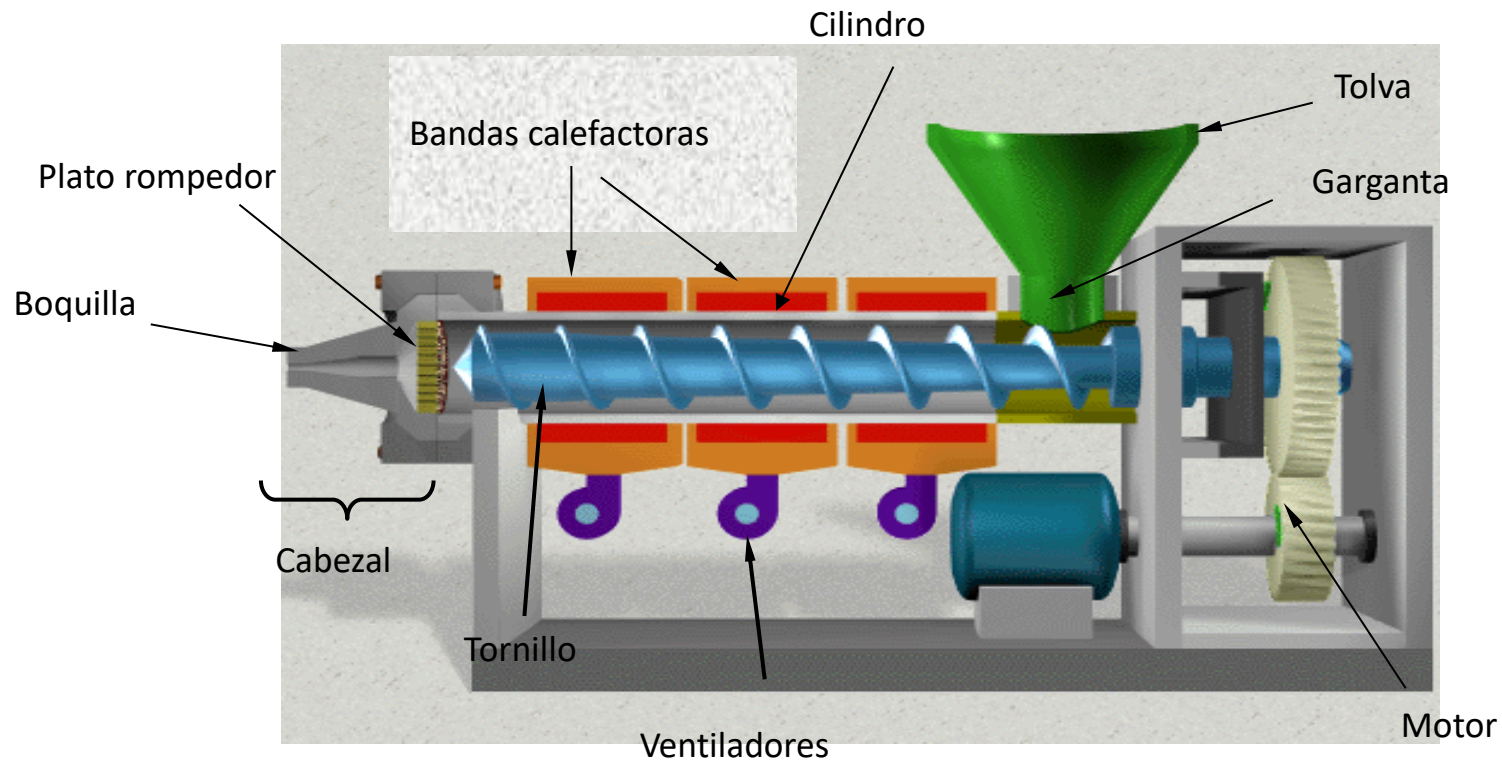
Extrusora de tornillo: Los componentes se integran formando 5 sistemas principales:
